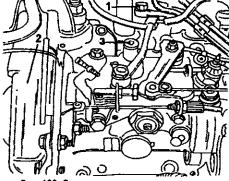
Расположение на топливном насосе высокого давления заглушки (1) контрольного отверстия верхней мертвой точки и кожуха зубчатого ремня (2). Заглушка (3) закрывает отверстие для регулировки топливного насоса высокого давления.
